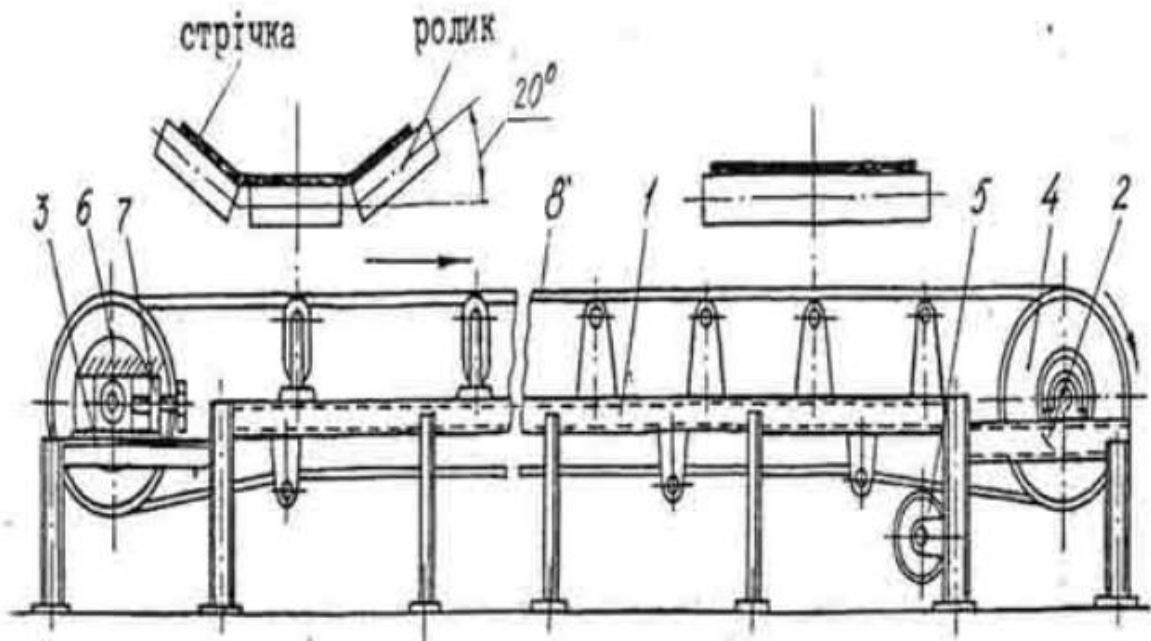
Схема стрічкового конвеєра: 1 – каркас; 2 – привідна станція; 3 – натяжна станція; 4 – привідний барабан; 5 – відхиляючий барабан; 6 – натяжний барабан; 7 – натяжний пристрій; 8 – стрічка.
